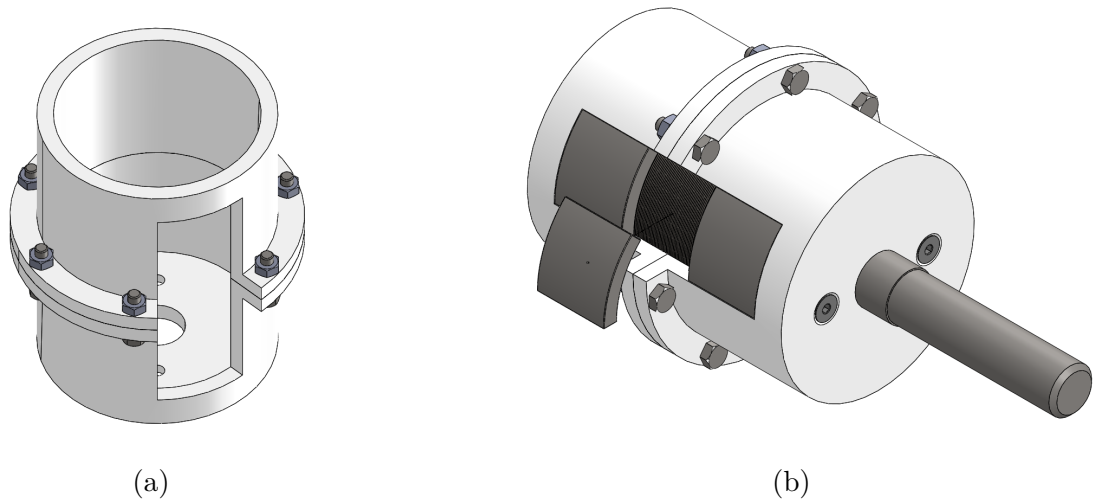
Outil d'assemblage des aimants du rotor haute vitesse : (a) outil (b) outil monté
